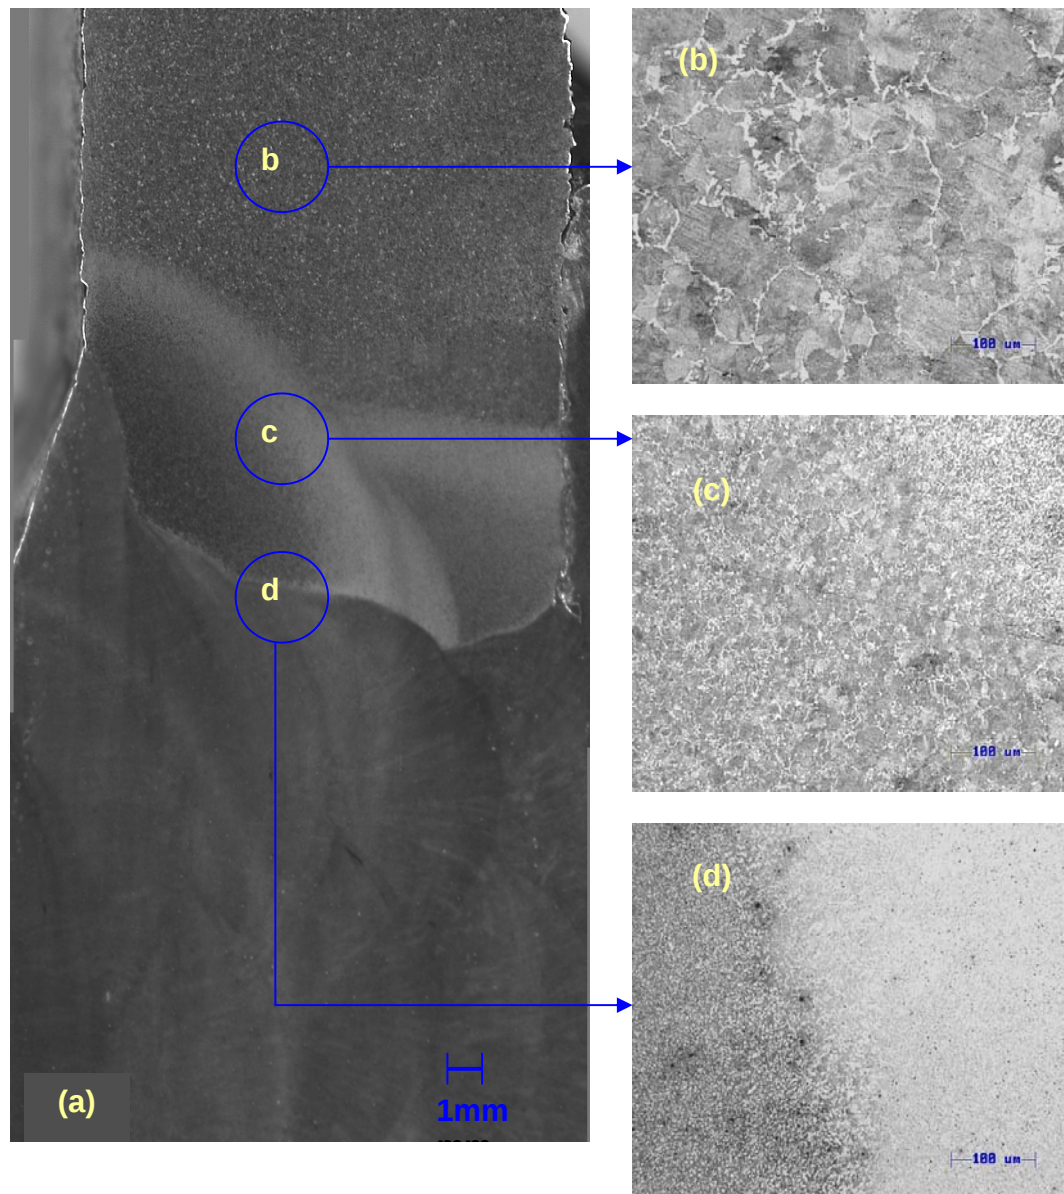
Fotomacrografía del Cordón de Soldadura, Corte Transversal. (a) Vista general. Detalles: (b) Material base, (c) Zona Afectada por el Calor e (d) Intercara de Metal Base Material de Aporte
